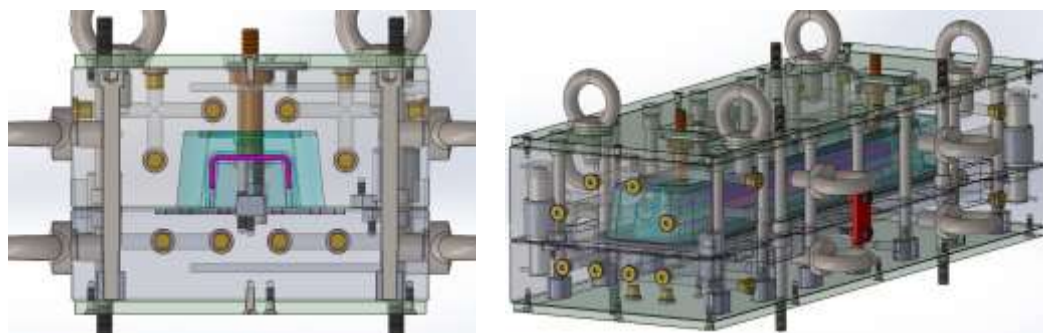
Molde de RTM en aluminio diseñado para la fabricación del perfil en U.
